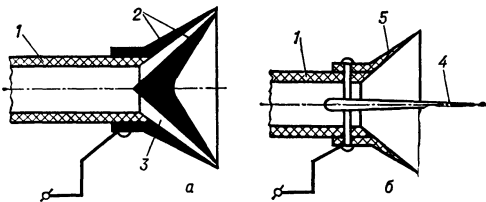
Схемы головок для контактной (а) и ионной (б) зарядки порошковой краски: 1 — корпус; 2 — металл. заряжающая головка; 3 — винтовые каналы; 4 — металл. коронирующая игла; 5 — кольцо.
